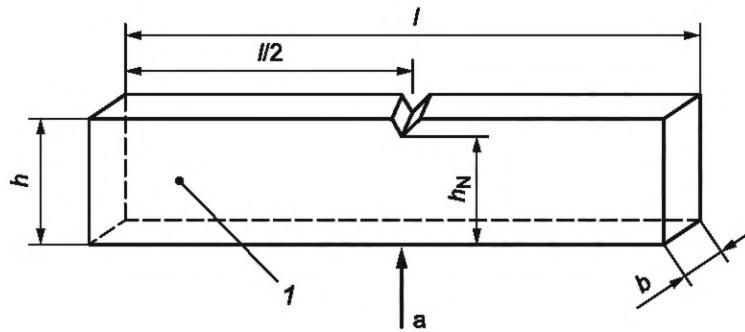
Удар по Шарпи плашмя образца типа 7
